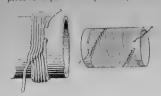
Способ намотки и общий вид готовой двуслойной катушки,
